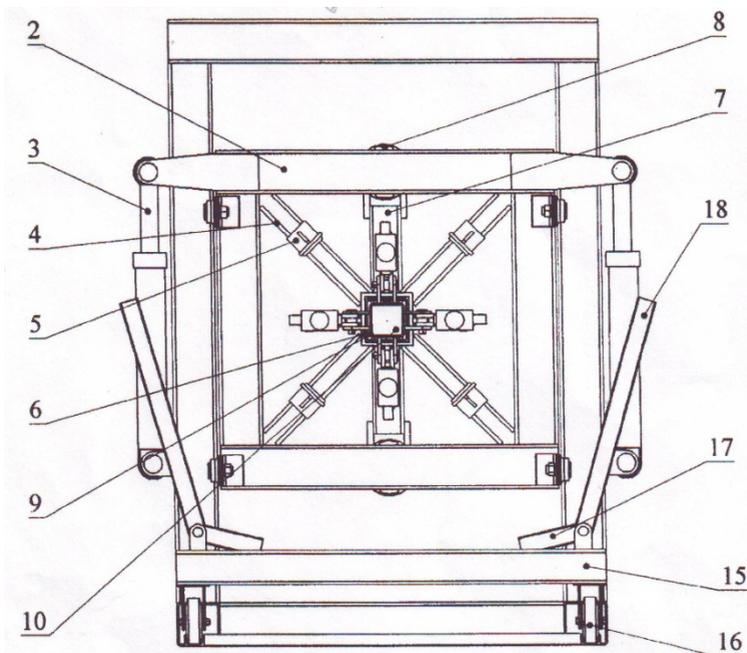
Стенд для монтажа и демонтажа шин с использованием тележки для передвижения колес
